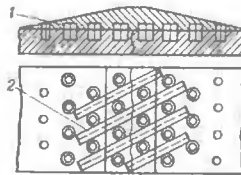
Схема розташування сталевих зв'язок у металі шва при холодному зварюванні чавуну:
